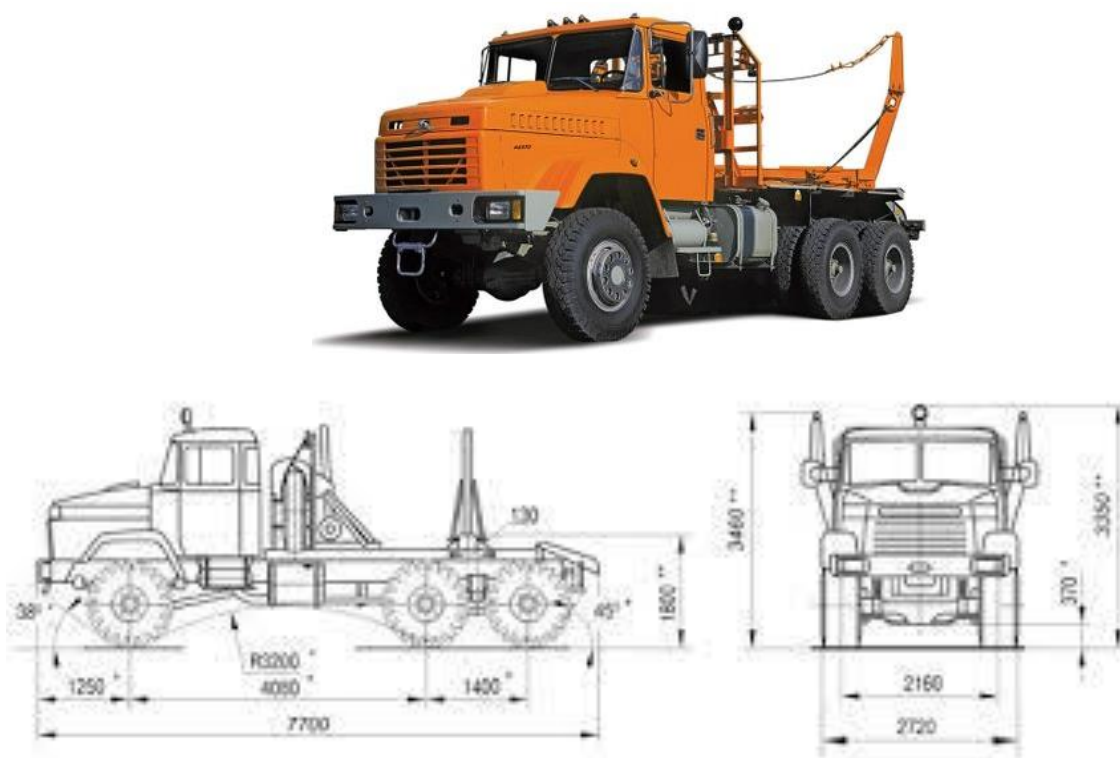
Загальний вигляд та габаритні розміри КрАЗ-6437
